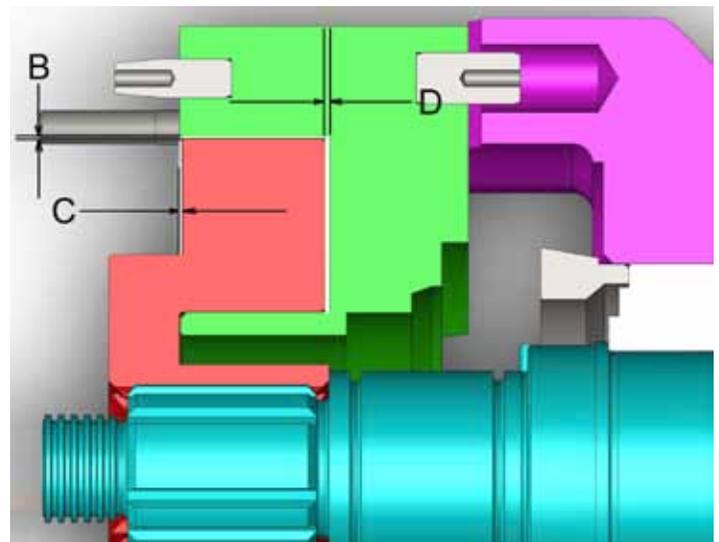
Rotor a Cuerpo Tolerancias
